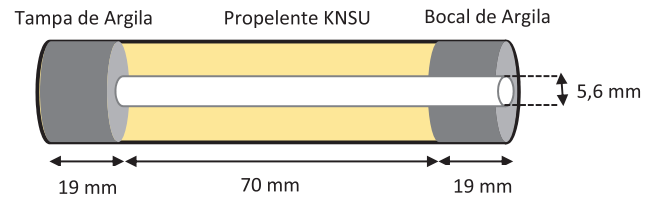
Ilustração das partes e dimensões do motor do minifoguete fabricado neste trabalho.
